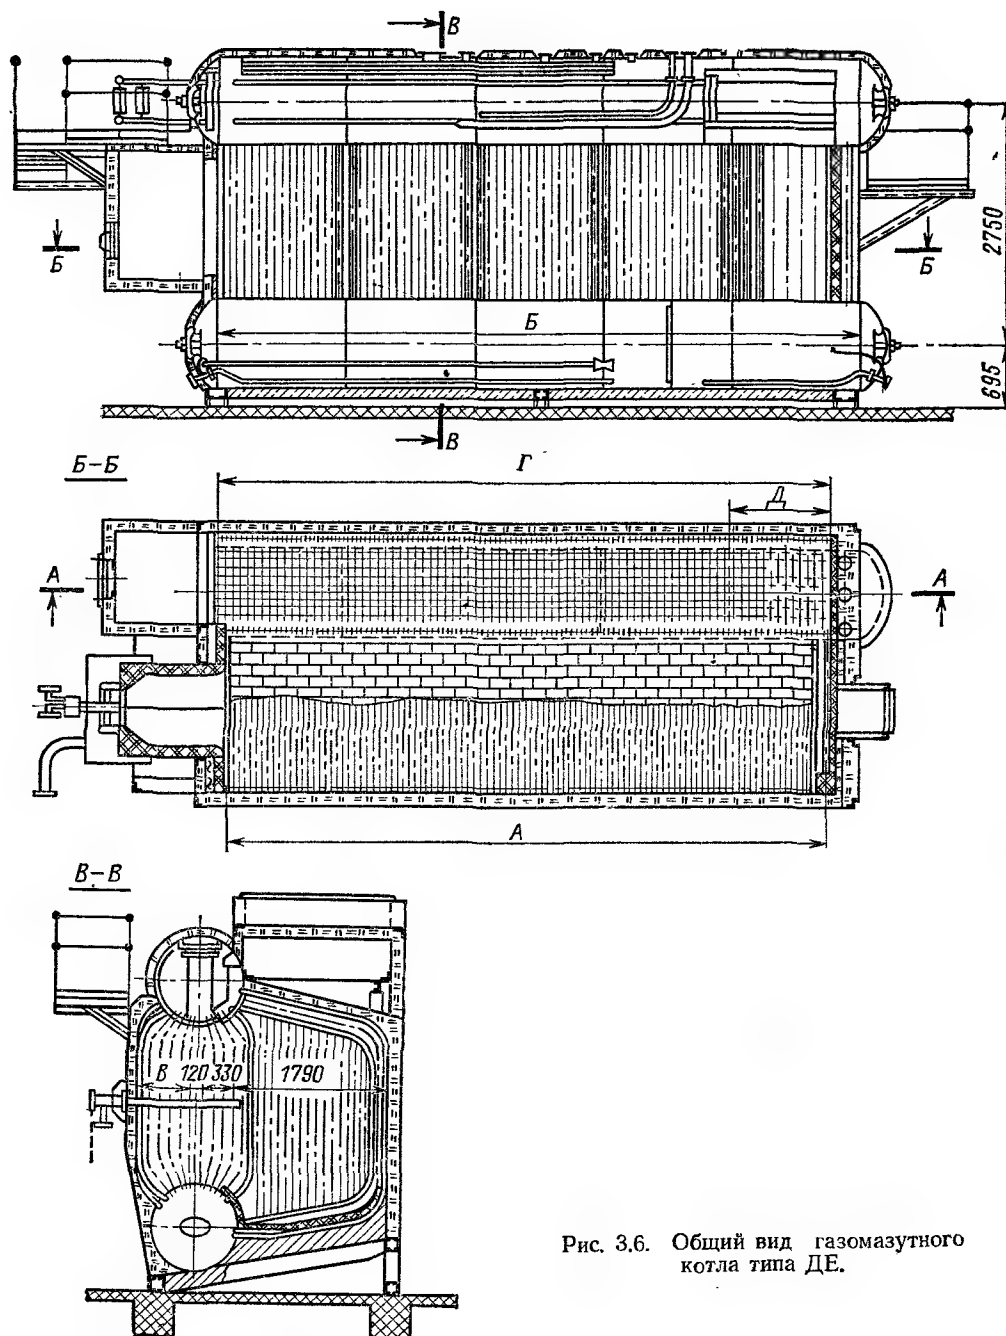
Общий вид газомазутного котла типа ДЕ.
